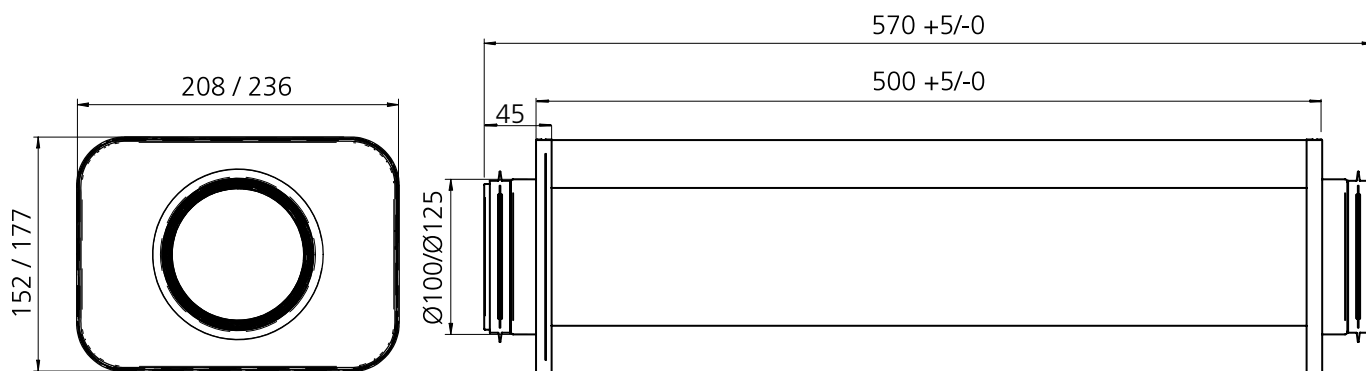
Maßskizze Schalldämpfer CLA Ø100-500 oder Ø125-500.
